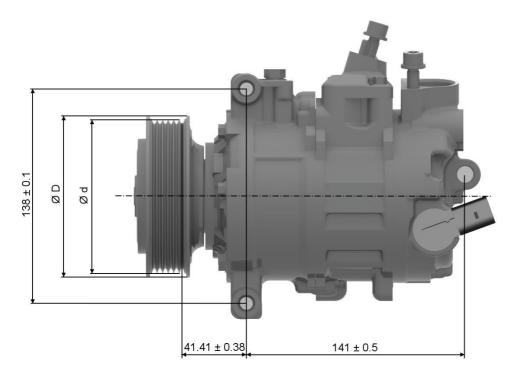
Dimensiones del compresor de agente frigorífico, diámetro de polea 110 mm (vista de perfil)
